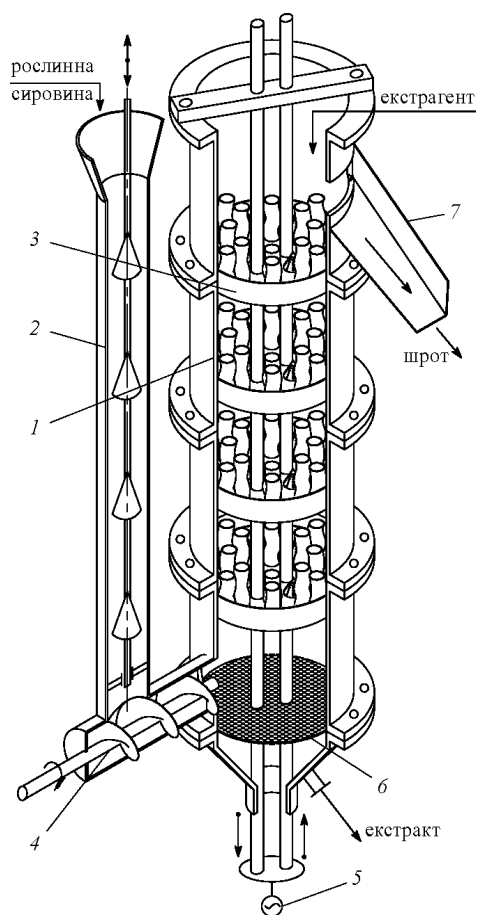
Загальний вигляд лабораторного віброекстрактора безперервної дії: 1 – корпус; 2 – завантажувальний пристрій; 3 – тарілки; 4 – шнек; 5 – вібропривід; 6 – фільтрувальна решітка; 7 – лоток.
